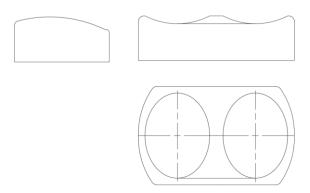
Rysunek elementu po pierwszym etapie obróbki
